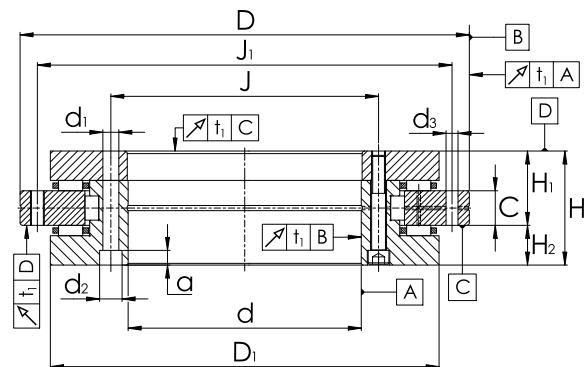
Axial-Schräggugellager, beidseitig wirkend
